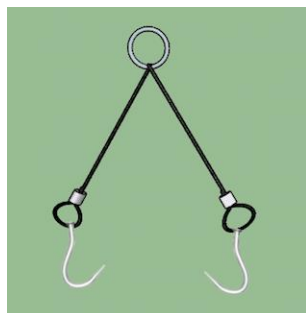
Ganchos de acero y tubo adecuado para crisol. Fuente: elaboración propia
